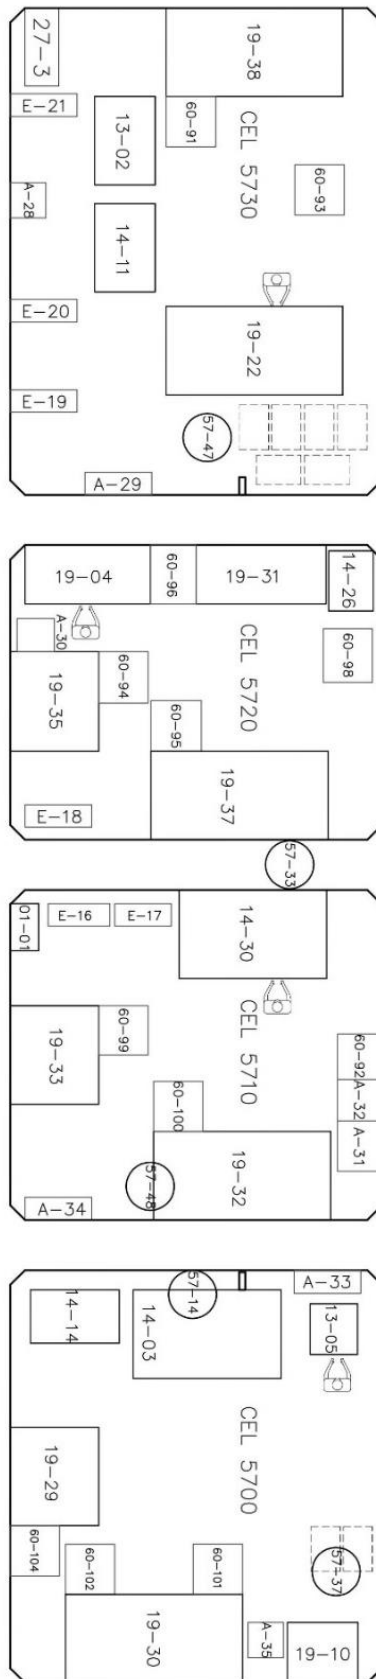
1 - Lay-out de celdas de mecanizado de piezas de aluminio
